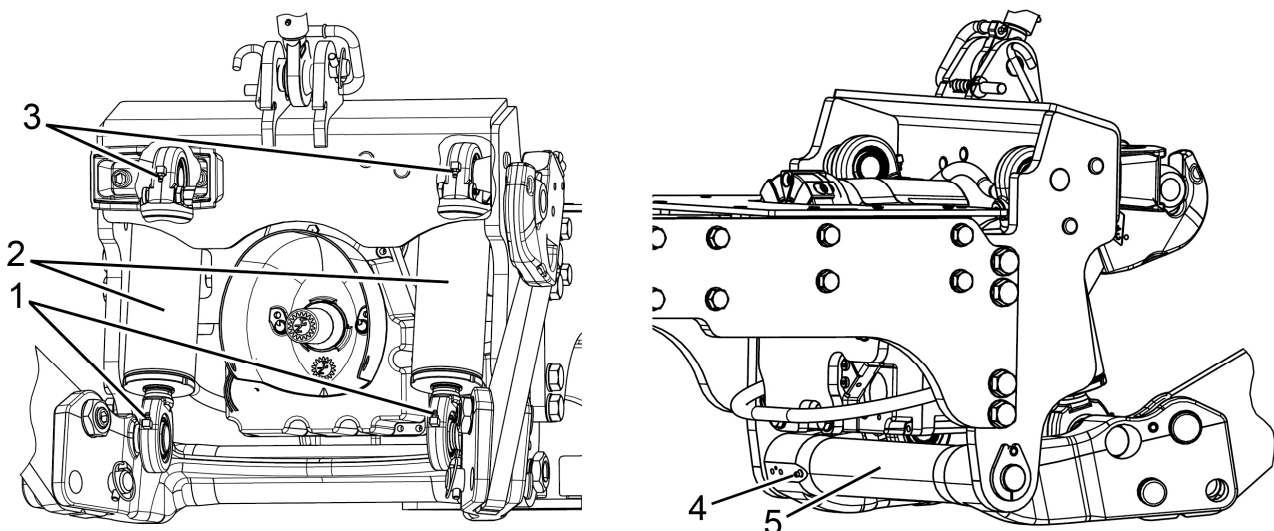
Смазка подшипников бугелей (вид снизу ПВМ)
